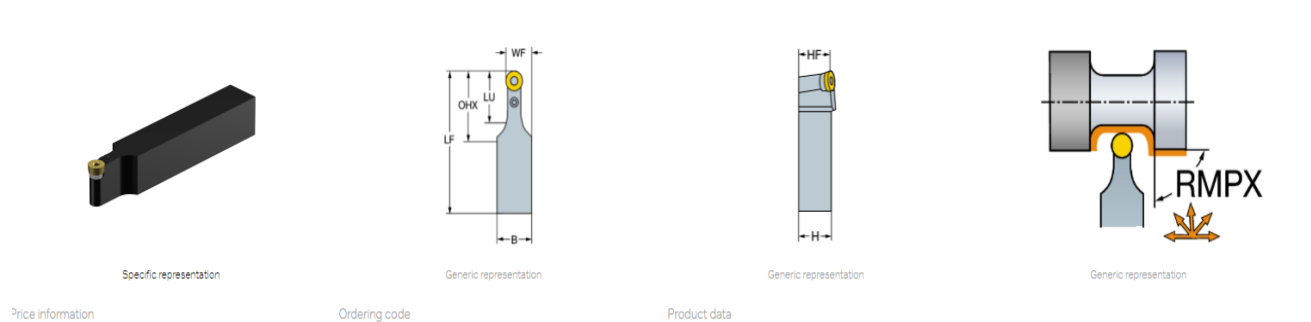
Різець торцевий PRDCN 2525M 12
